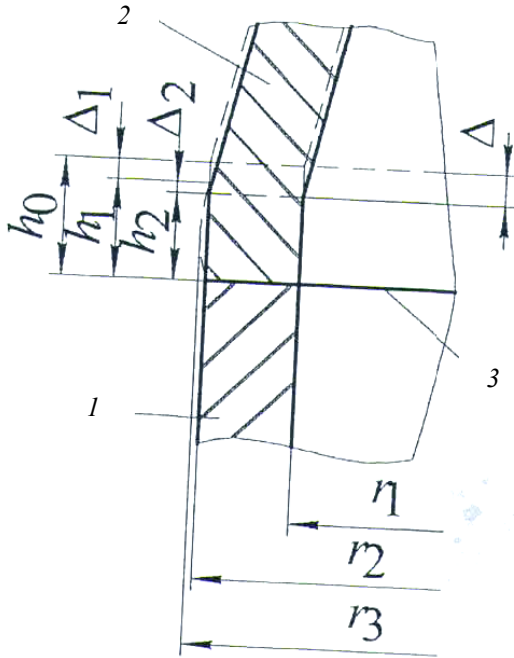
Расчетно-технологическая схема соединения: 1, 2 – обечайки; 3 – поверхность сварки
